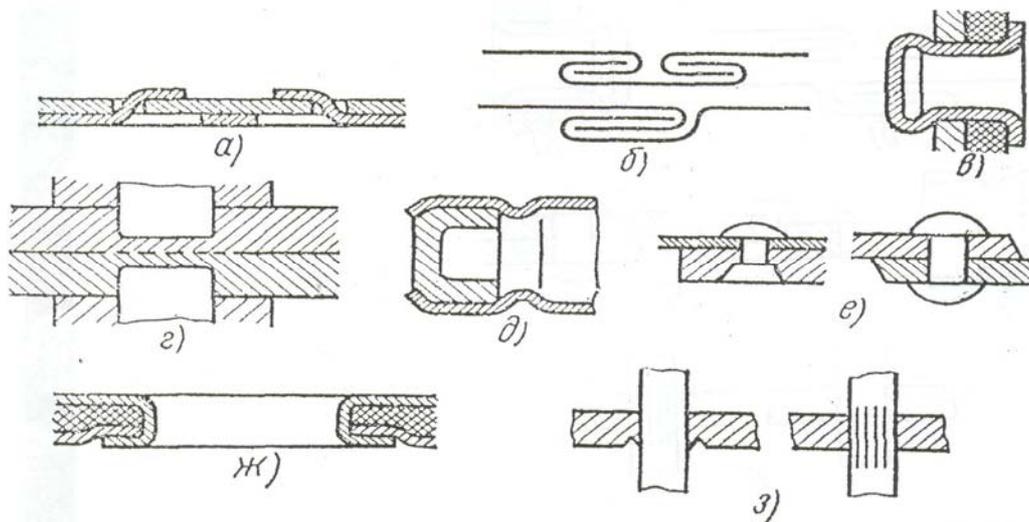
Штампосборка лапками (а), в замок (б), раздечей (в), холодной сваркой (г), обжимкой (д), клепкой (е) и др.
